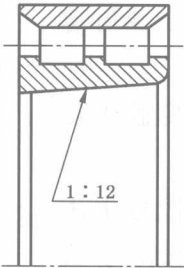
圆锥孔双列向心短圆柱滚子轴承
